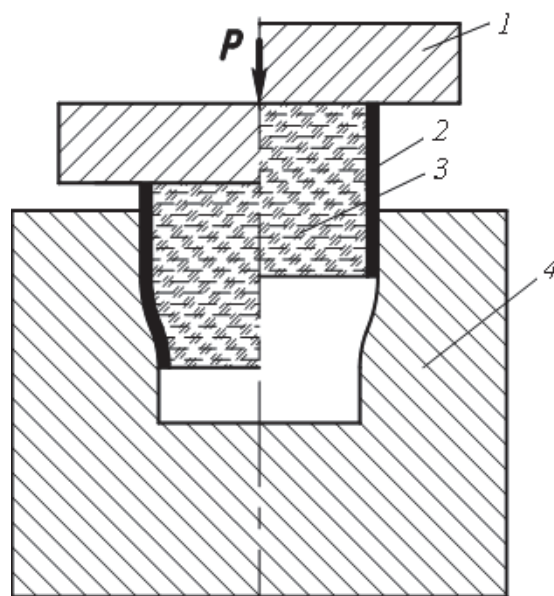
Штамп для обжима трубчатой заготовки с использованием ледяного стержня
